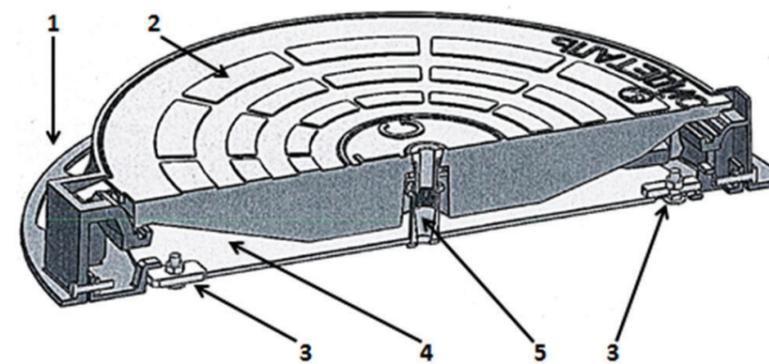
Разрез устройства УЗЛ-Т ССД с видом запорного механизма в закрытом положении: 1 – чугунная крышка; 2 – корпус люка; 3 – задвижки, зафиксированные в закрытом положении; 4 – нижняя стальная крышка; 5 – запорный механизм.
